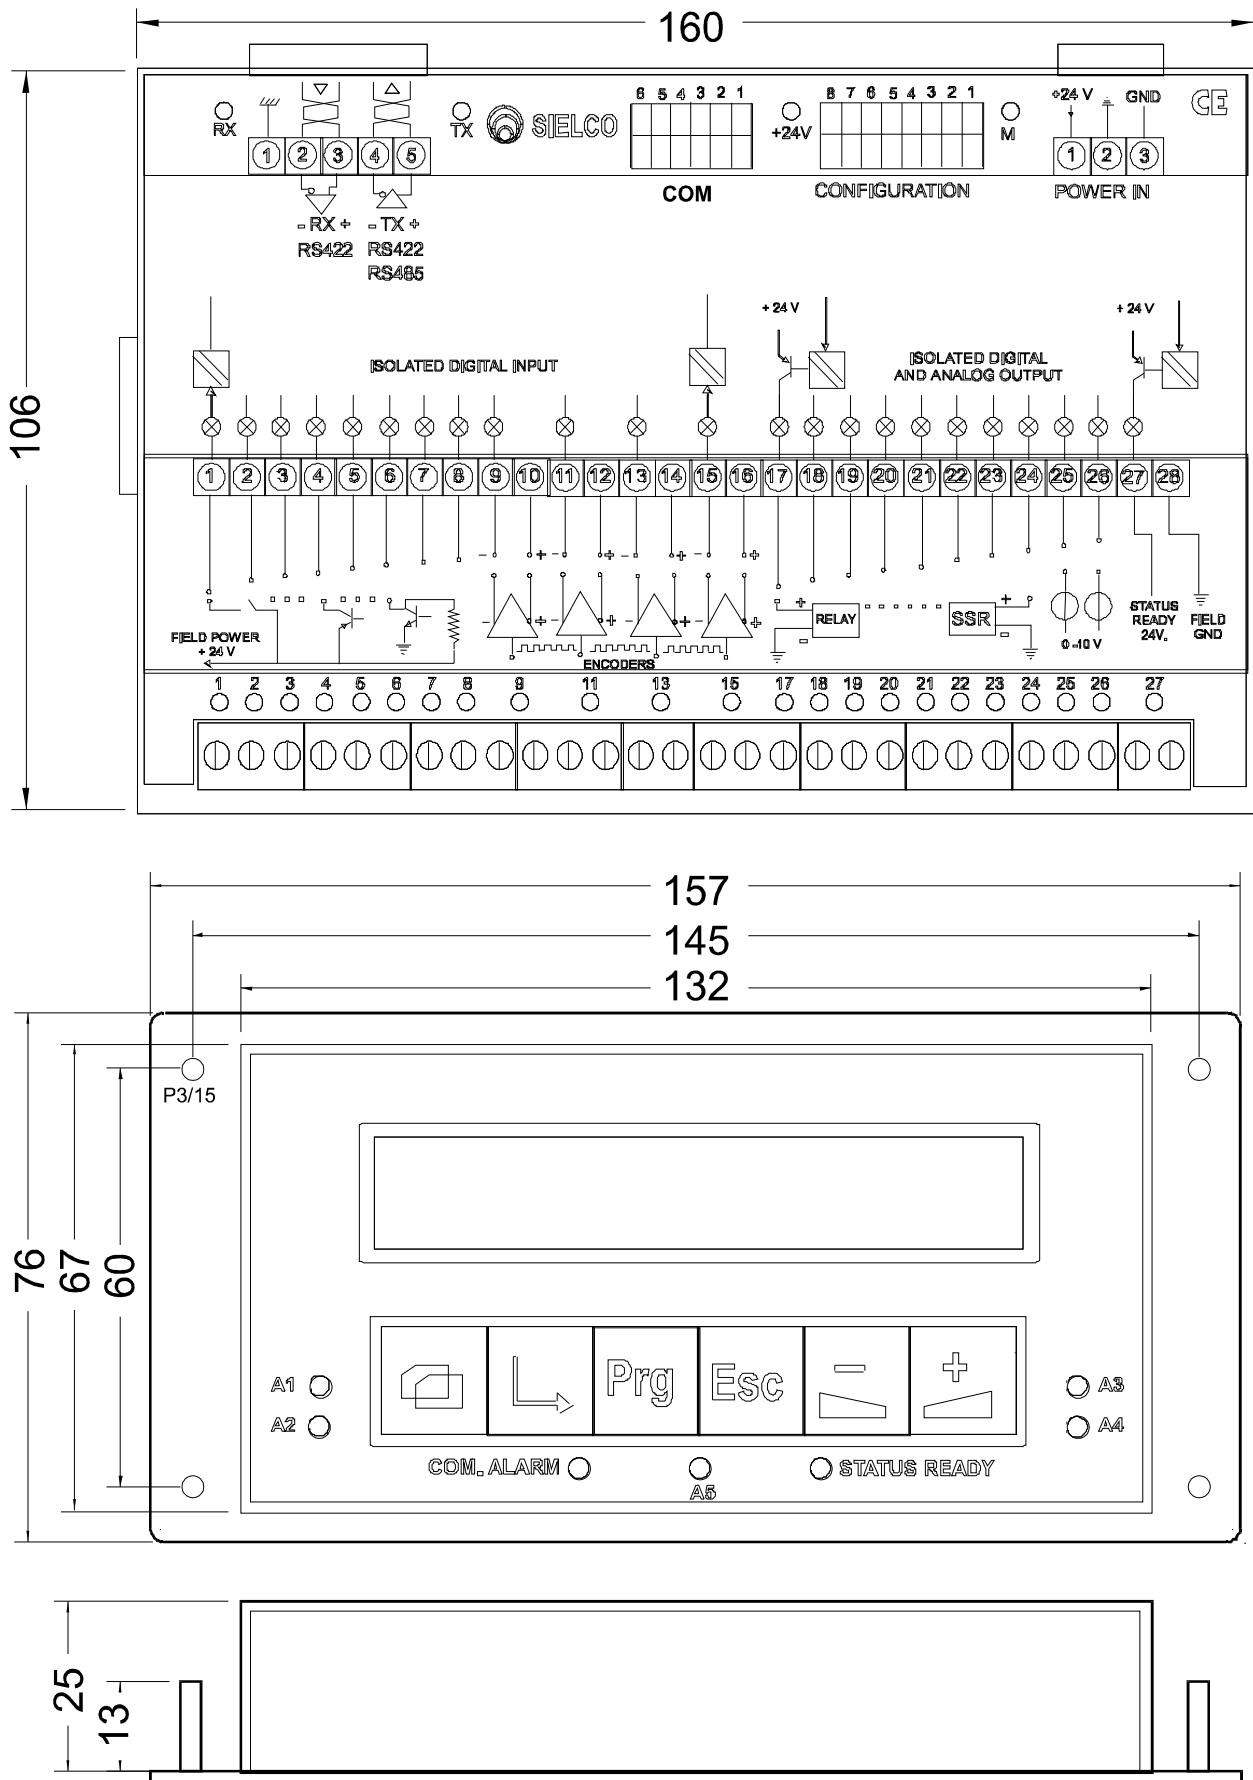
Dimensioni del modulo D1-35 e del pannello operatore F1-10
